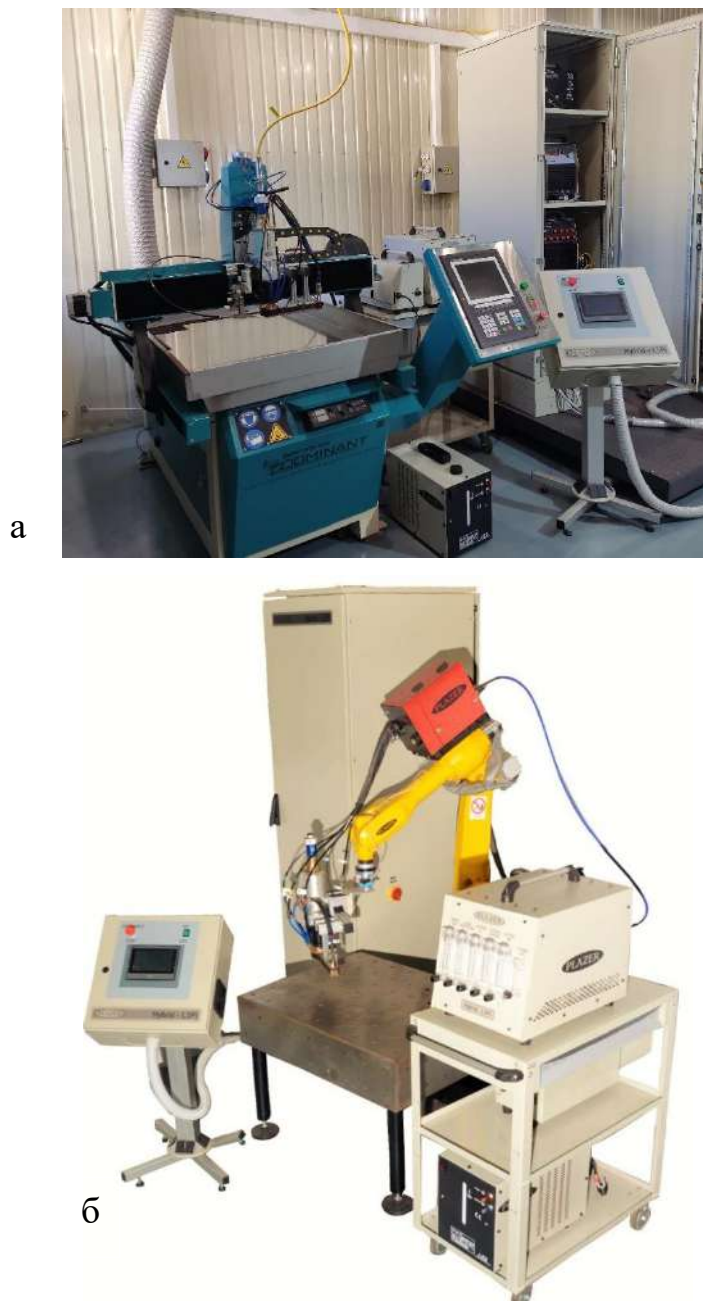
Загальний вигляд установки для лазерно-плазмового зварювання PLAZER Hybrid L5Pl. (а - з трьохкоординатним столом; б – з антропоморфним роботом)
